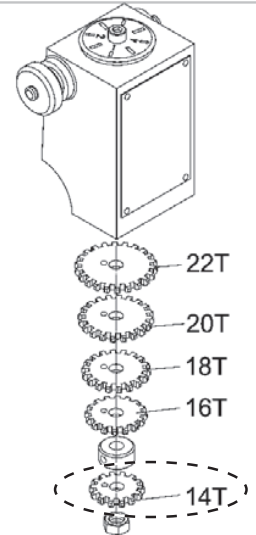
Voorbeeld van draadsnijlklok - 14 T
